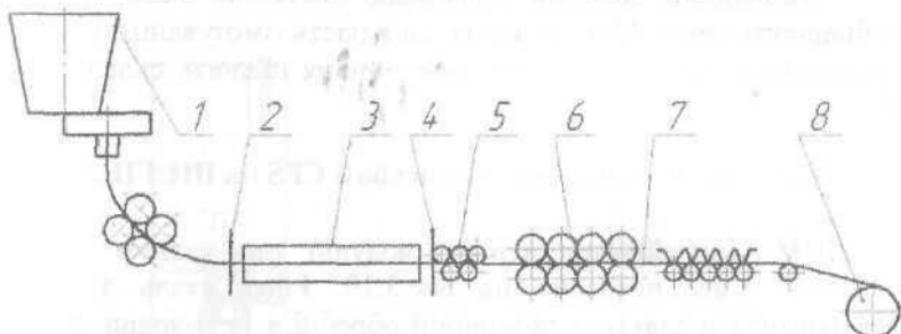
Однорівчаковий ЛПК типу CSP: 1 – МНЛЗ; 2 – ножиці; 3 – піч вирівнювання температури; 4 – ножиці; 5 – окалиноламач; 6 – прокатний стан (чистова група); 7 – ділянка охолоджування штаб; 8 – моталка.
